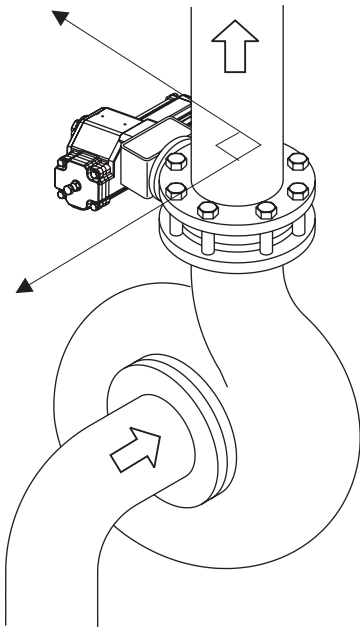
Installation d'une vanne papillon au refoulement d'une pompe centrifuge
